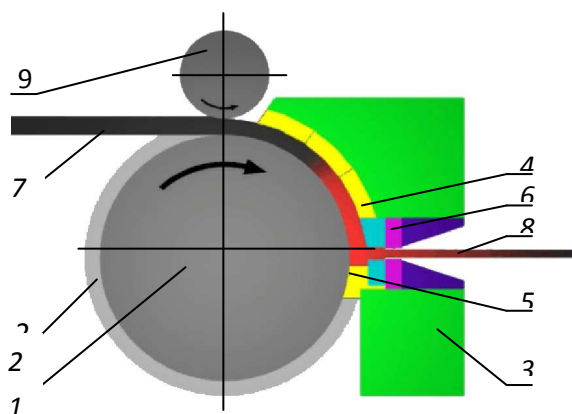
Принципиальная схема реализации процесса непрерывного прессования по способу Конформ: 1 - рабочее колесо; 2 - кольцевая канавка; 3 - башмак; 4 - кольцевая вставка; 5- вставка; 6 - матрица; 7 - заготовка; 8 - изделие; 9 - валок
